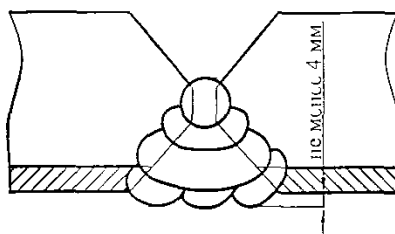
Порядок наложения швов при автоматической сварке под флюсом
